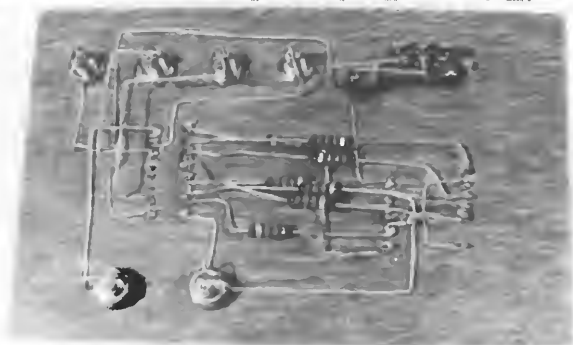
Parte dei collegamenti del dispositivo di foto 10
